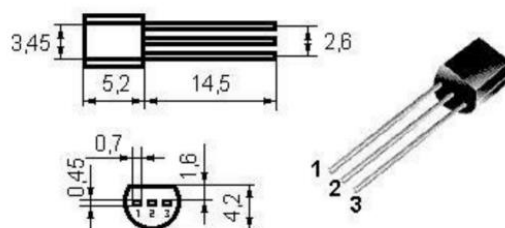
Схематичний вигляд та габарити стабілізатора 78L05
